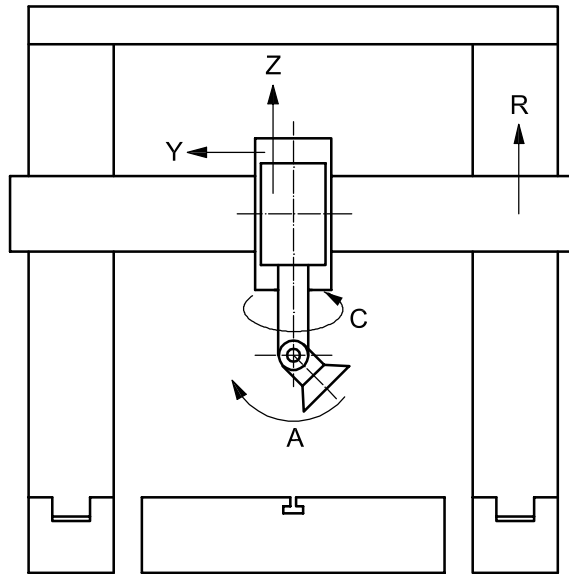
Machine à une tête de fraisage pivotant autour des axes A et C
